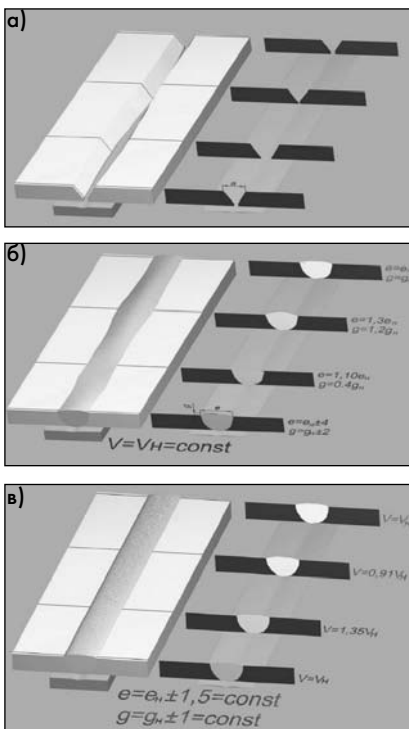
Типичные дефекты сборки (а) и формирование сварного шва с адаптивным управлением процессом сварки (б) и без адаптивного управления (в)
